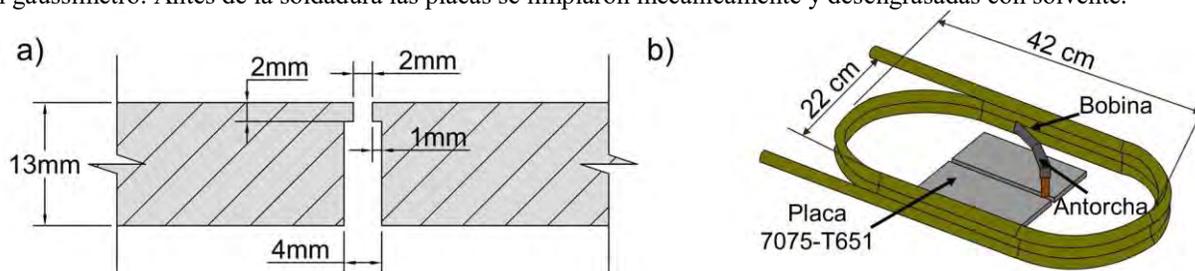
Juntas soldadas a) Preparación con técnica AEIM. b) Configuración experimental de soldadura.
